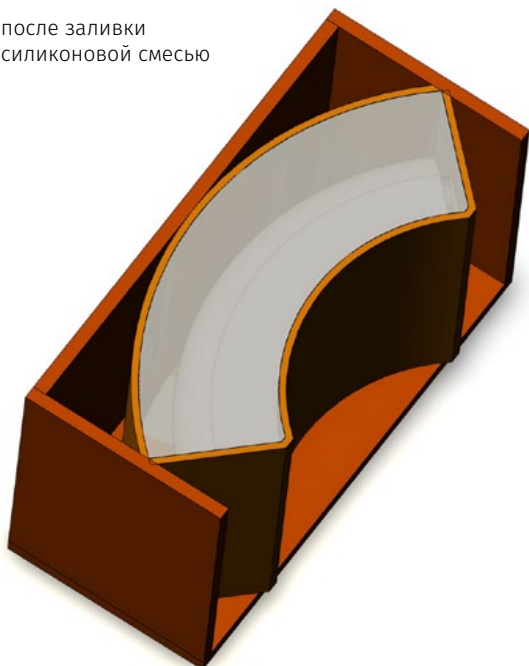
Поддерживающий внешний короб с пластиковыми перегородками и мастер-моделью
